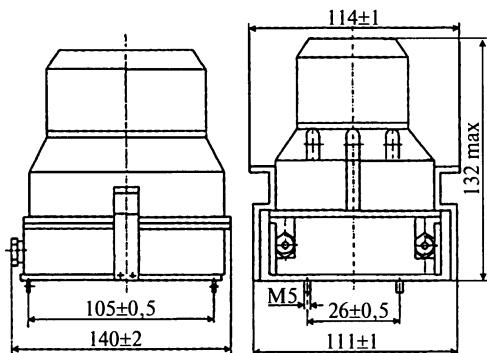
Извещатель пожарный комбинированный ИПК-ТУ
